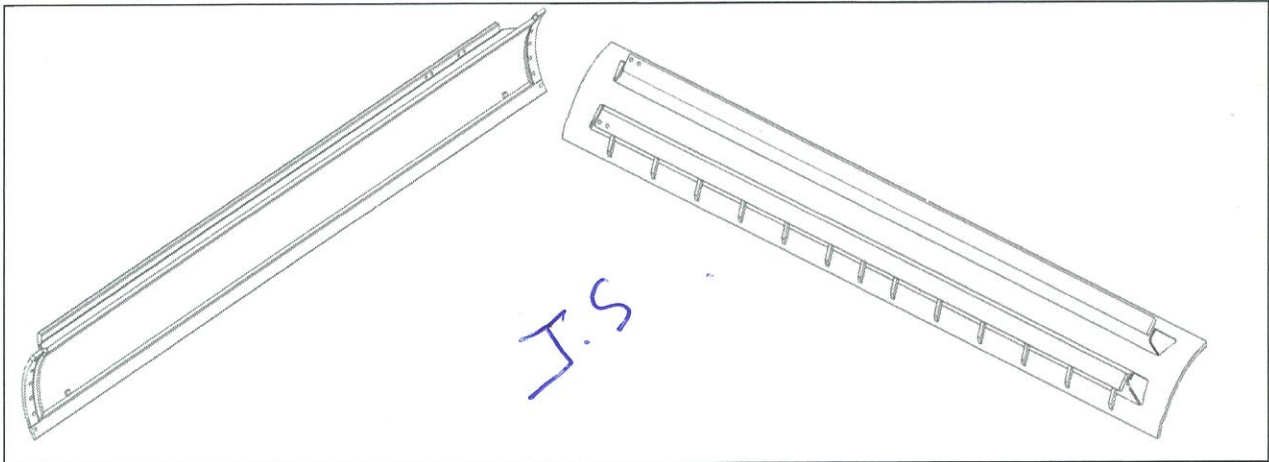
Revisar fisuras, marcas de golpes, desgaste anormal en las estructuras
